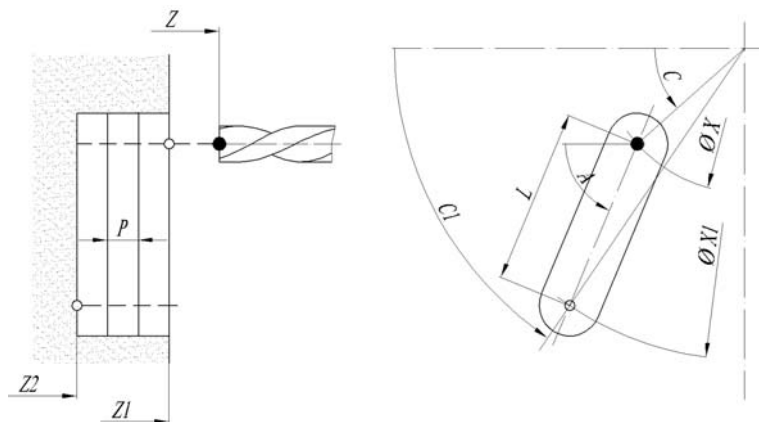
Цикл фрезерования линейного паза на торцевой поверхности (G791)
